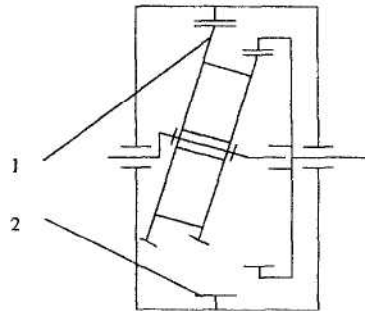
Кінематична схема планетарної прецизійної передачі:
